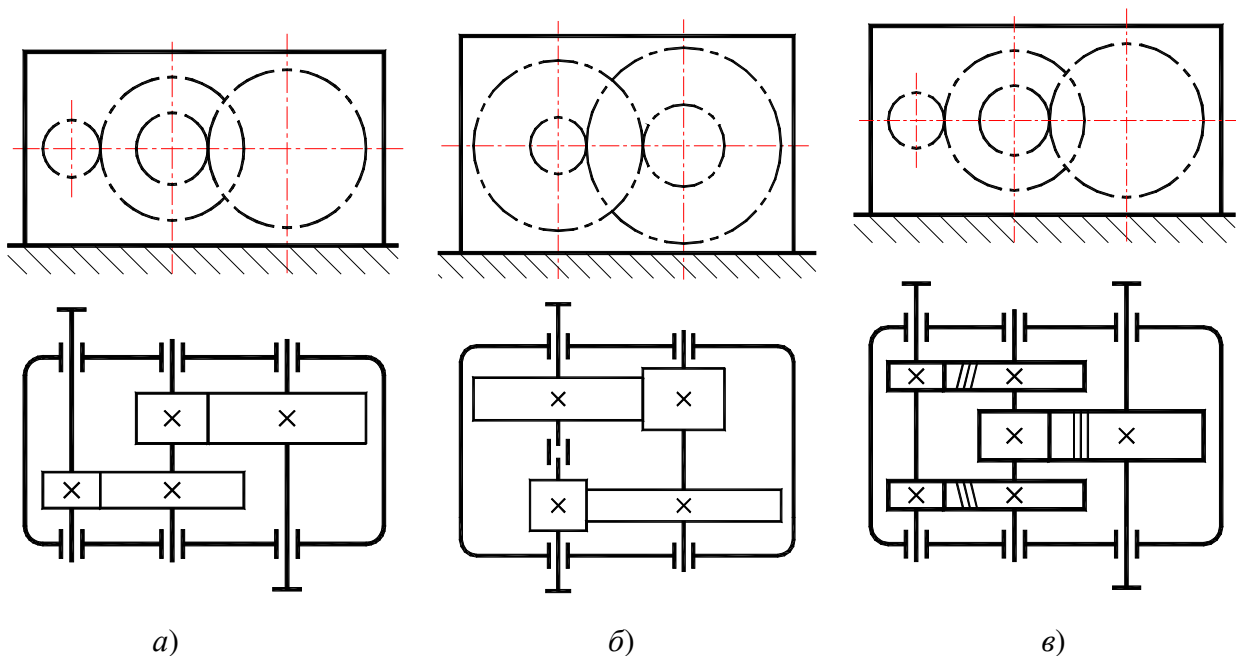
Кинематические схемы цилиндрических двухступенчатых редукторов: а) развернутая схема; б) соосная схема; в) схема раздвоенный шеврон
